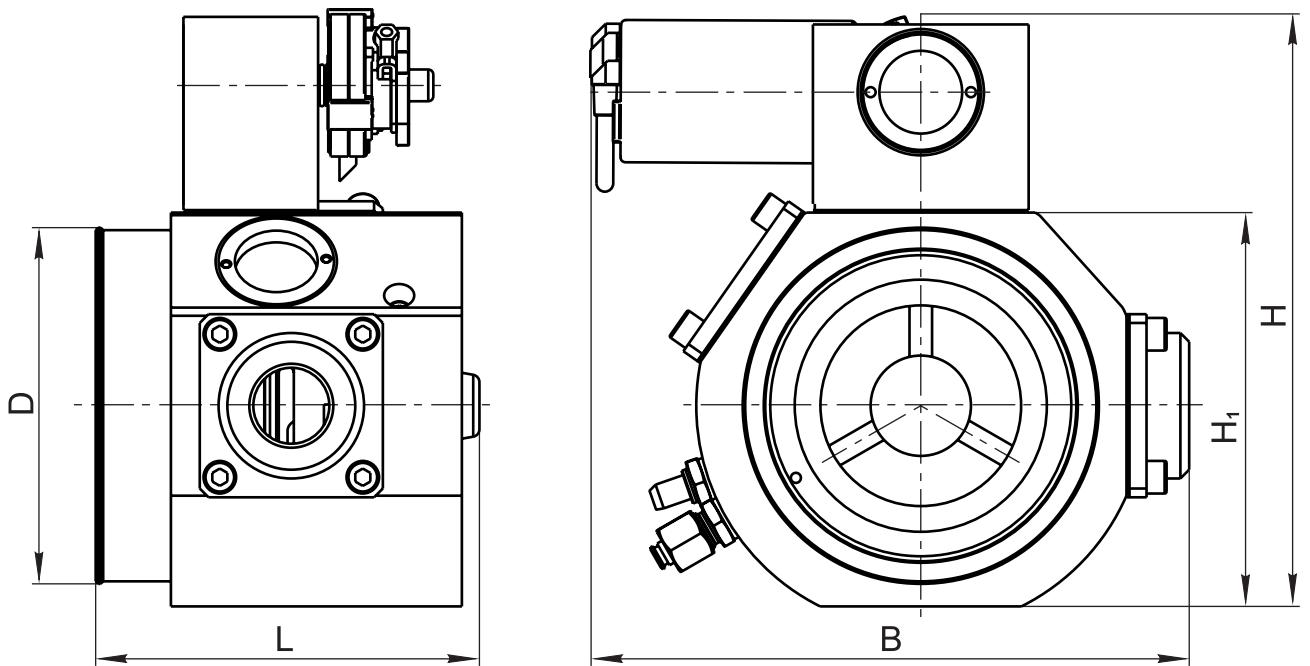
Габаритные и присоединительные размеры для смесителей типа СГ...-М
